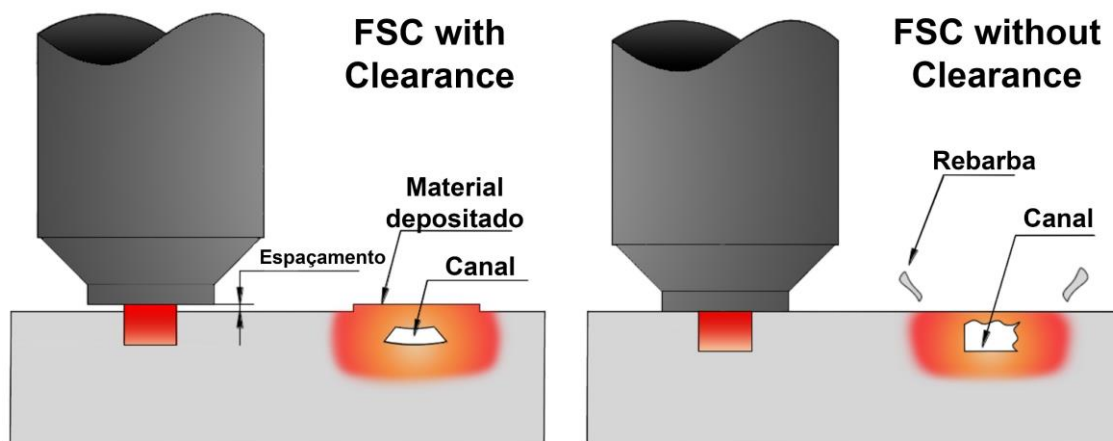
Representação esquemática das técnicas FSC *with Clearance* (à esquerda) e FSC *without Clearance* (à direita), adaptado de [2].
